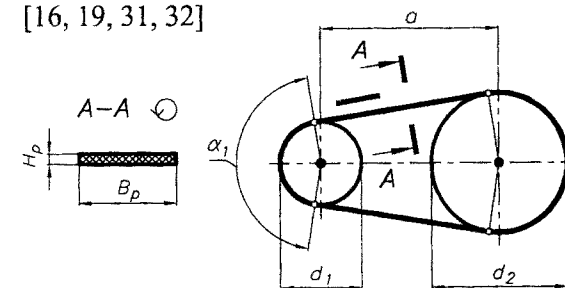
Схема и основные размеры плоскоремненной передачи
